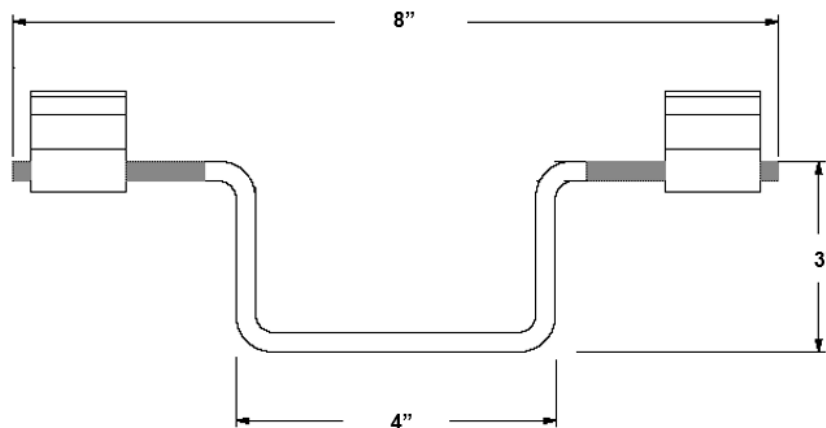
Dimensiones mínimas en mm del Estribo tipo palanca
